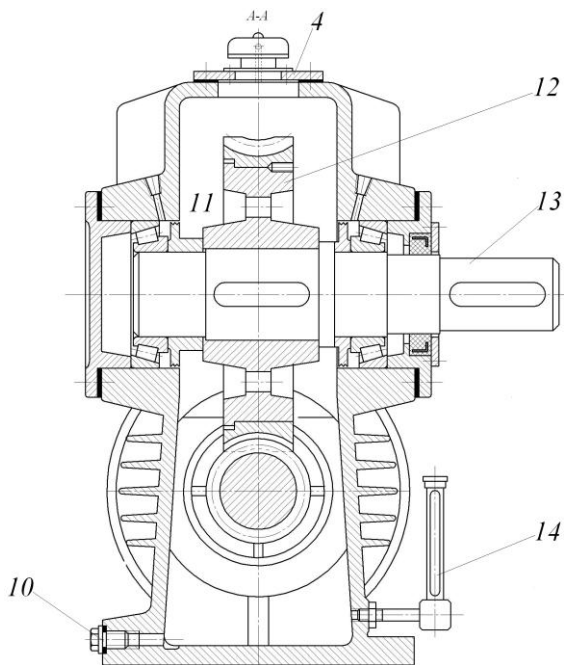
Редуктор червячный одноступенчатый с вентилятором (вид сбоку)
